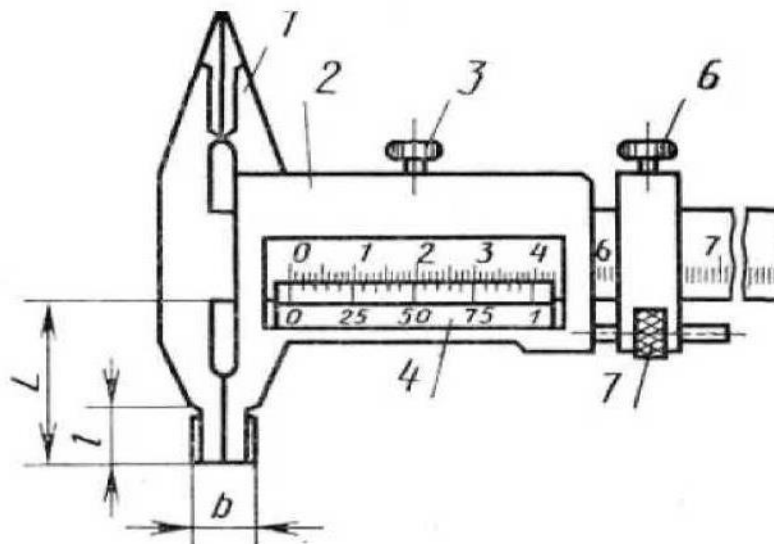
Общий вид штангенциркуля: 1 - измерительные губки; 2 - подвижная рамка; 3 - стопорный винт на подвижной рамке; 4 - нониус; 5 - винт на штанге;
